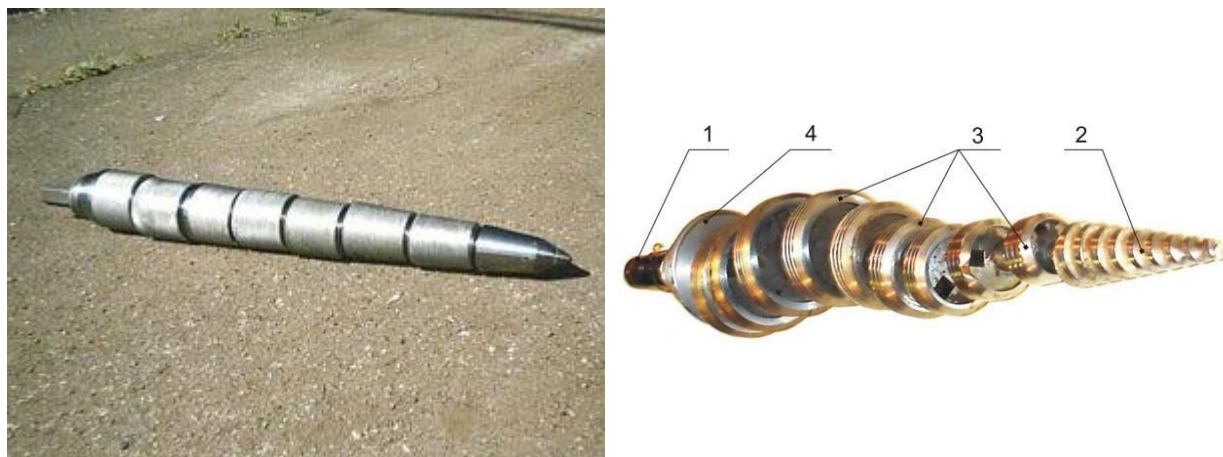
Розкати: а) – з конічними робочими елементами, б) – з короткими циліндричними робочими елементами на яких нанесена гвинтова поверхня
